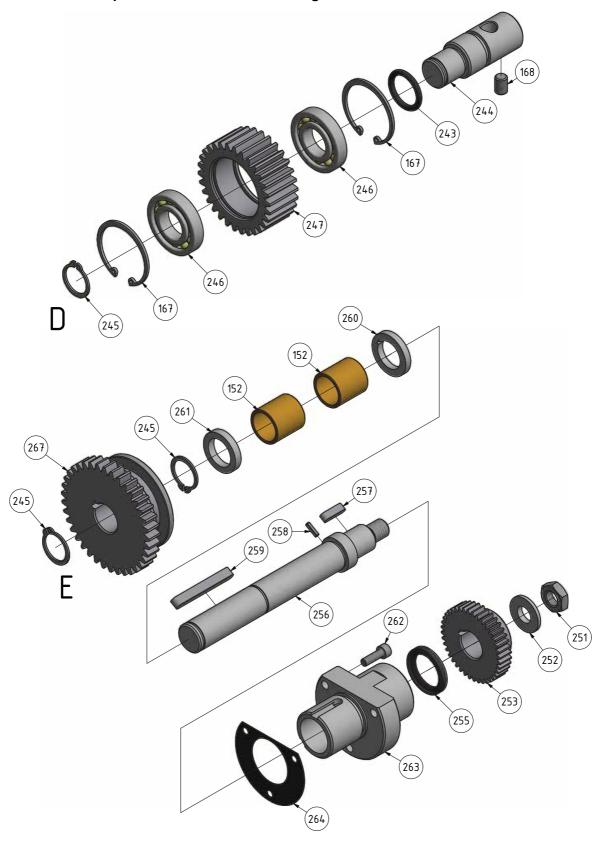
Getriebe Spindelstock 5-6 - Headstock gear 5-6
